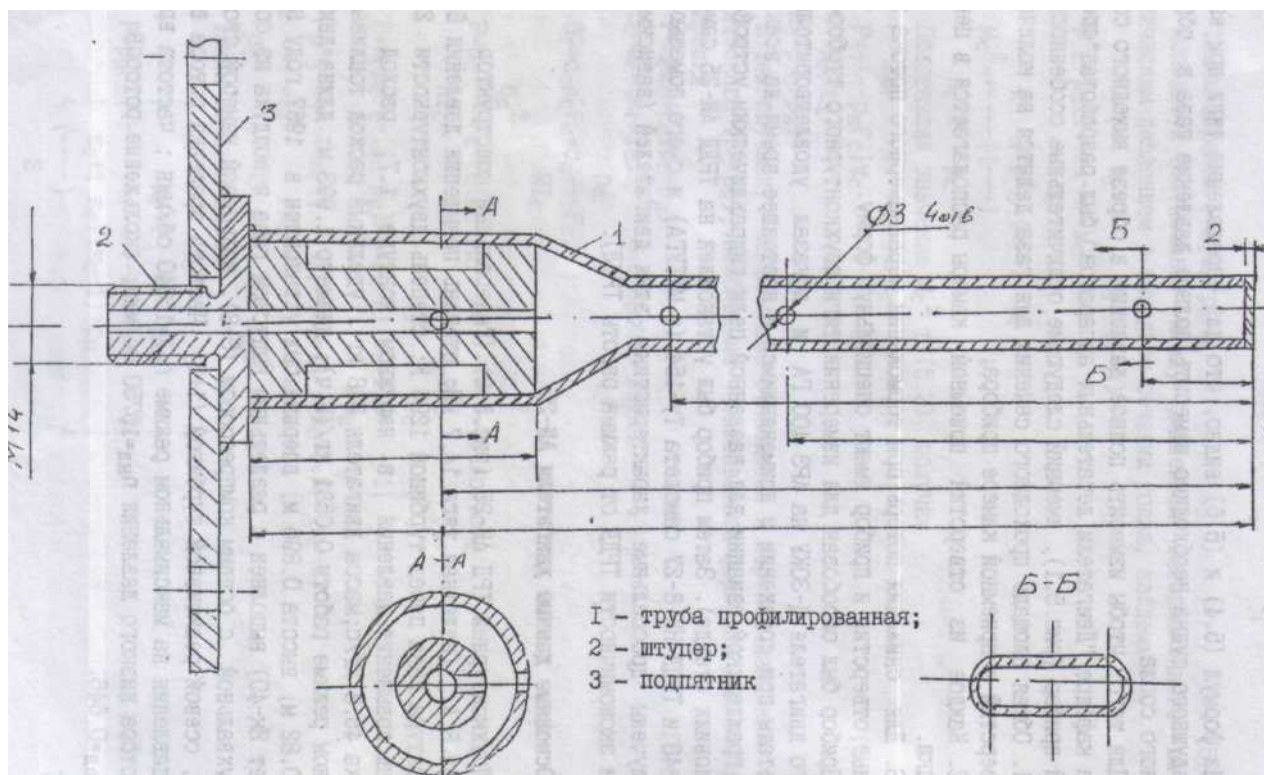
Конструкция прибора для измерения полного давления в выходном сечении реактивного сопла ТРД
